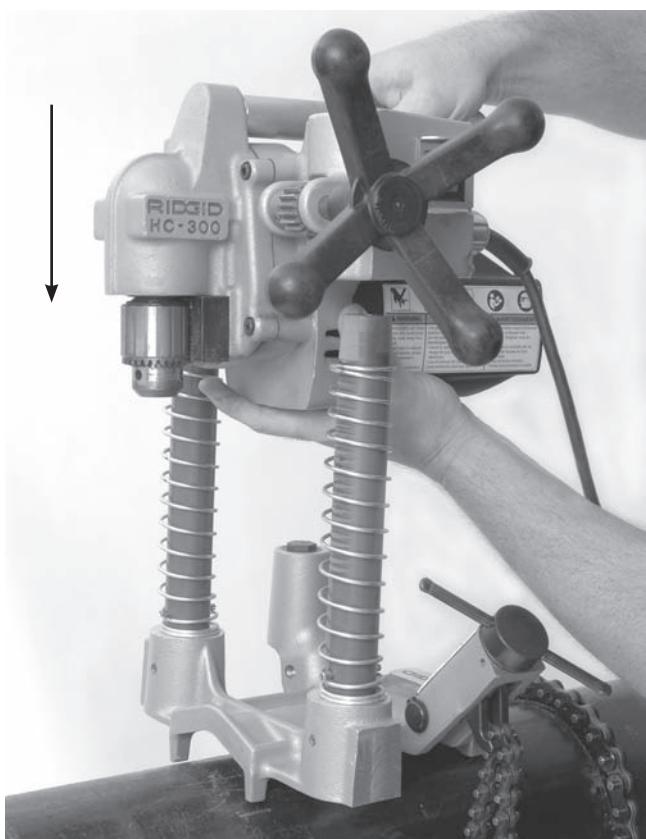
Fixação do Conjunto do Motor ao Conjunto da Base da HC-300
